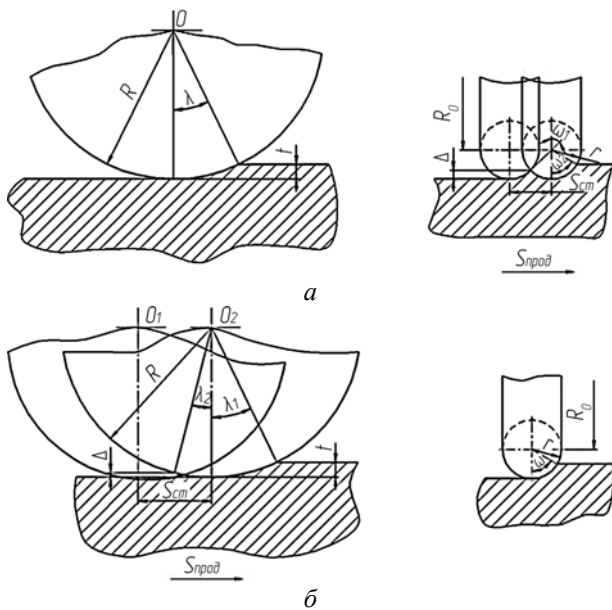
Схемы плоского шлифования тороидальным кругом для двух схем формообразования: а – поперечная; б – продольная
